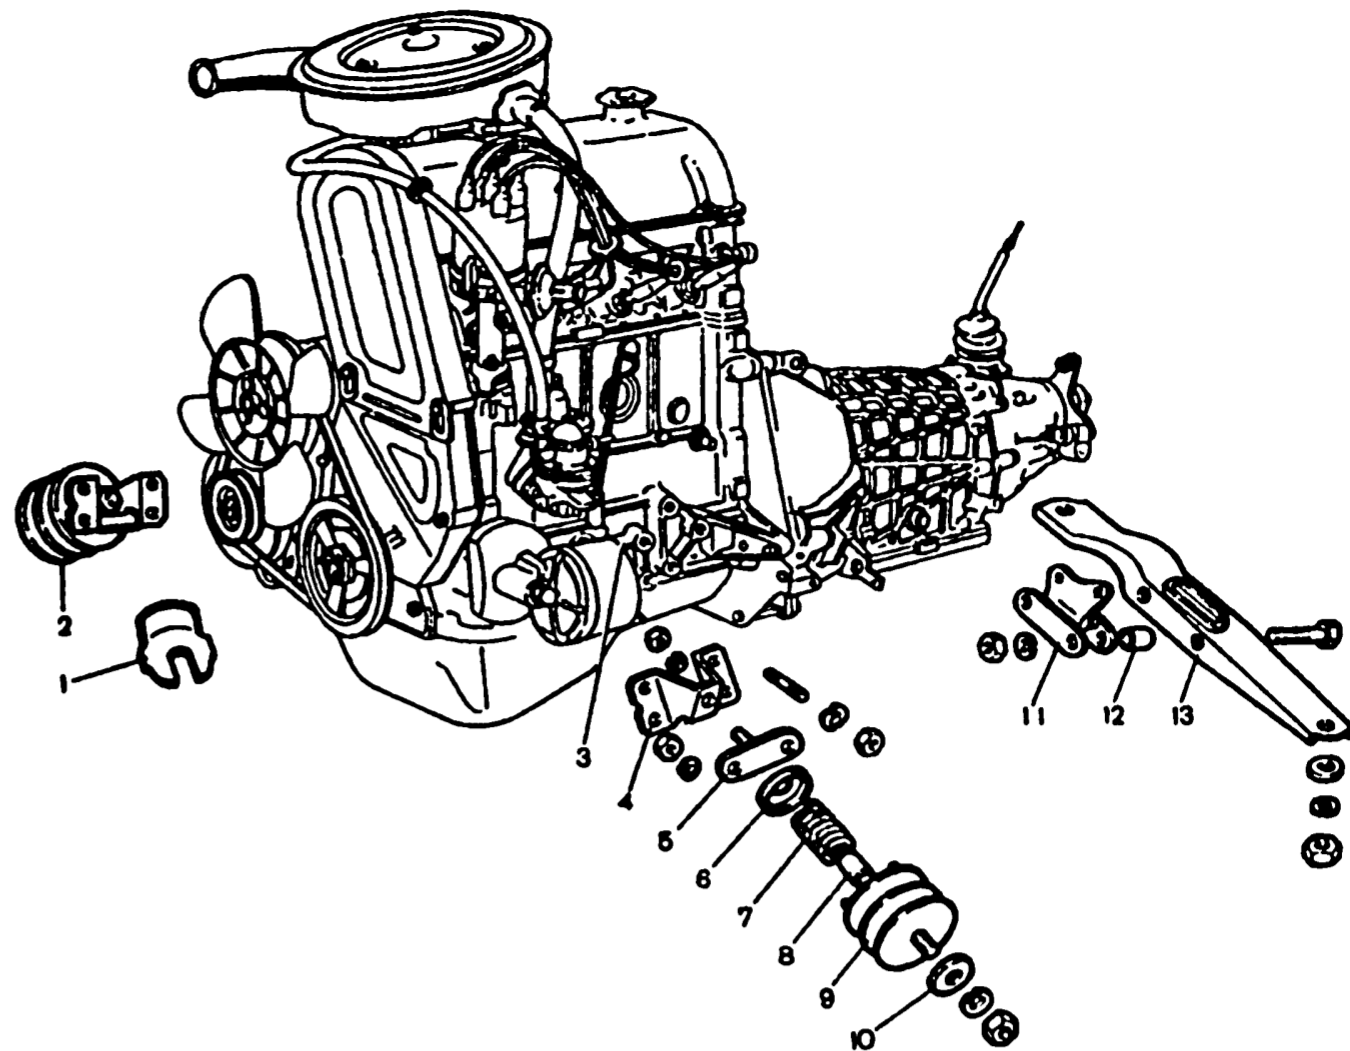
Подвеска двигателя: 1 - кожух опоры; 2 - опора передней подвески двигателя; 3 - фланец блока цилиндров; 4 - кронштейн; 5 - промежуточная пластина; 6 - изолирующее пластмассовое кольцо; 7 - пружина опоры; 8 - буфер; 9 - подушка опоры; 10 - шайба; 11 - опора задней подвески двигателя; 12 - дистанционная втулка; 13 - поперечина задней подвески двигателя
